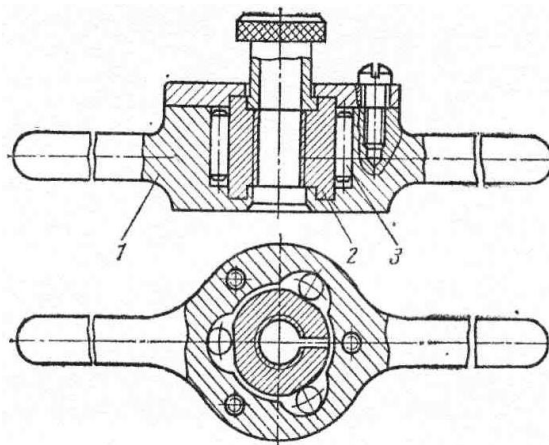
Пристрій з циліндричною, розрізною гайкою: 1- корпус; 2- гайка; 3- затискні ролики
